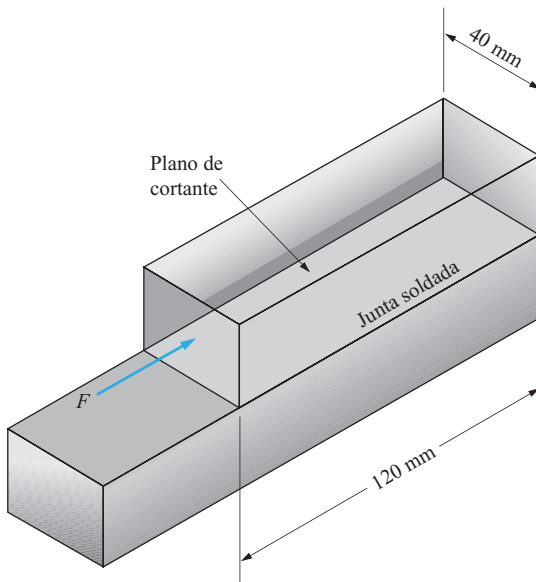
Componentes soldados para el problema 1-68.
